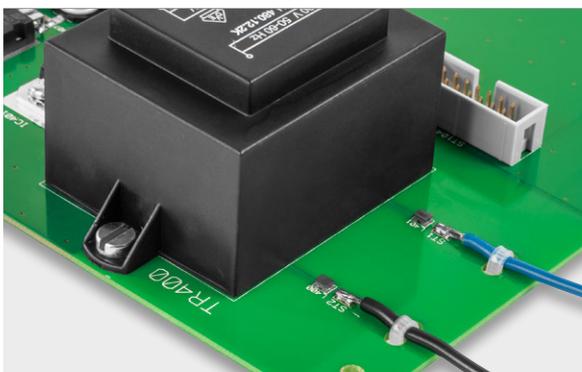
Detailbild zum Einbau der primärseitigen Zuleitungen des Netztransformators
